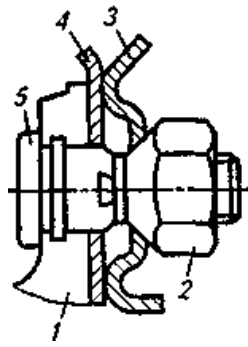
Крепление колеса легкового автомобиля: 1 — ступица; 2 — гайка; 3 — диск колеса; 4 — тормозной барабан; 5 — болт
